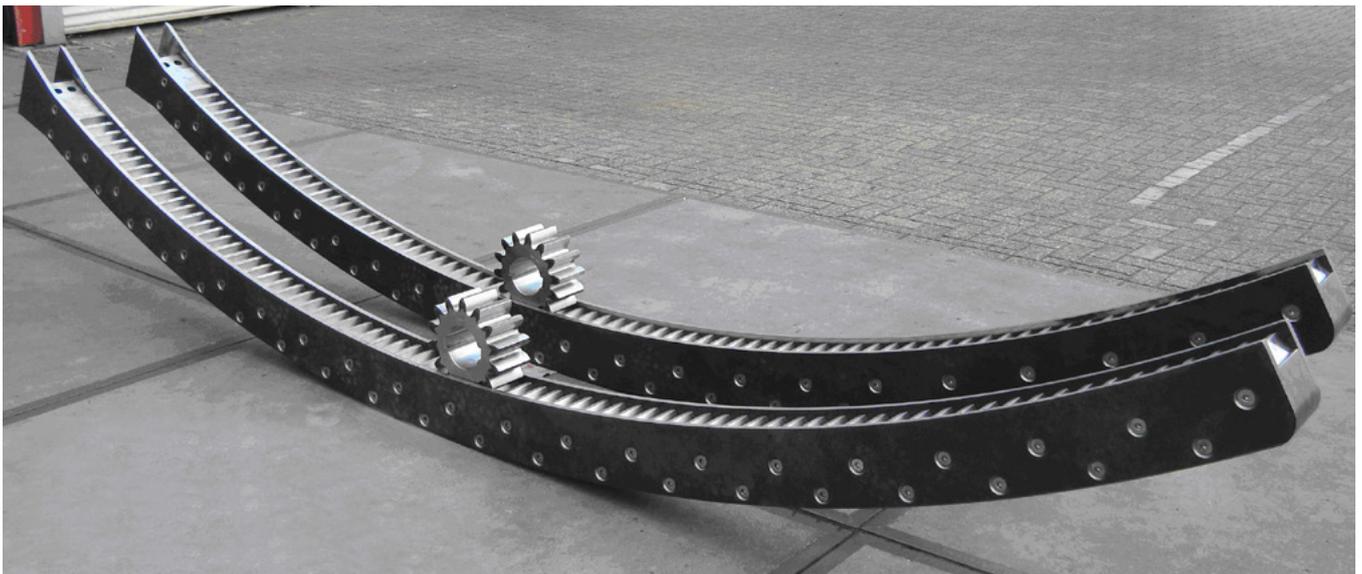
Zahnstange für eine Brücke aus Toolox® 44.
